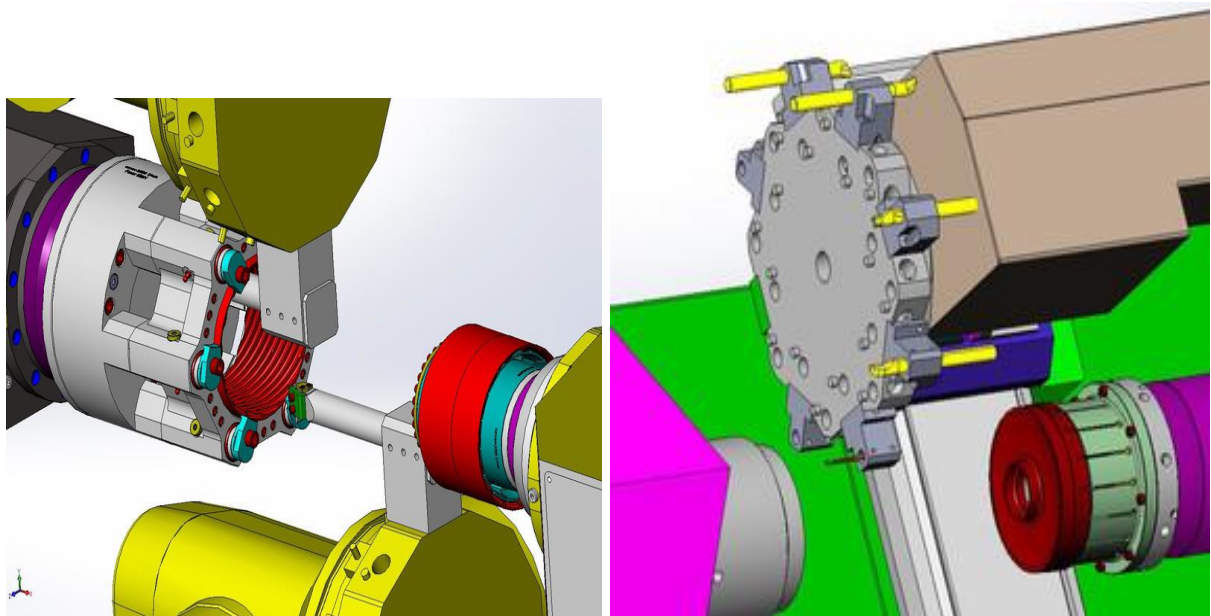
Схеми обробки на токарних верстатах з проти шпинделями
